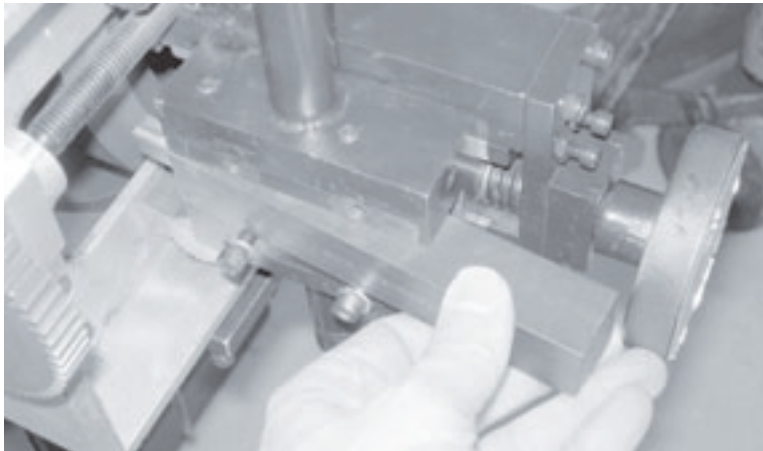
Отверните фиксирующую пластину резцедержателя винты для возможности посадки резцедержателя в суппорте.
